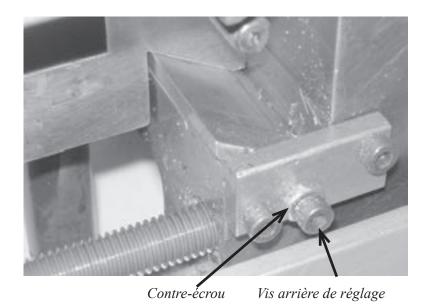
Vis arrière de réglage du serrage du porte-outil mâle.
